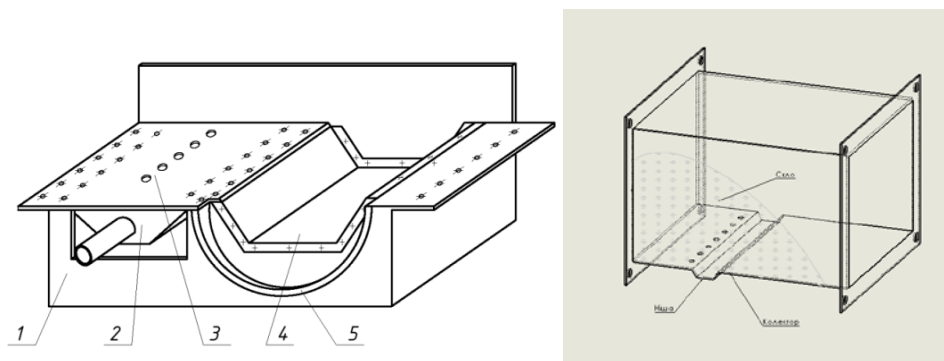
Блок установки елементів струменево-нішевого стабілізатора полум'я: 1 – корпус блоку; 2 – розбірний газовий колектор; 3 – система круглих отворів для паливоподачі; 4 – нішева порожнина; 5 – напівфланець оглядового скла
